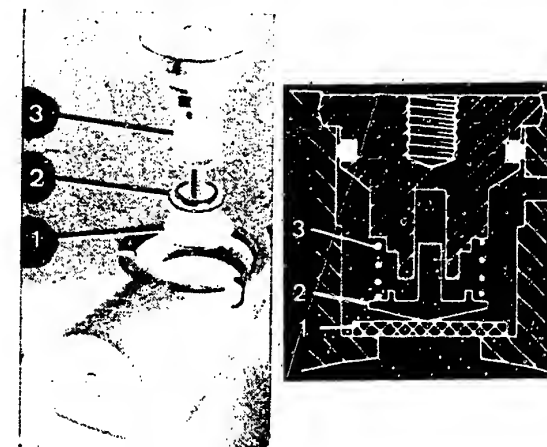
Das Rückschlagventil besteht aus: 1 Ventilplättchen – 2 Führungsteil – 3 Ventulfeder. Vorsicht: Beim Ein- und Ausbau keine scharfen Werkzeuge verwenden.
